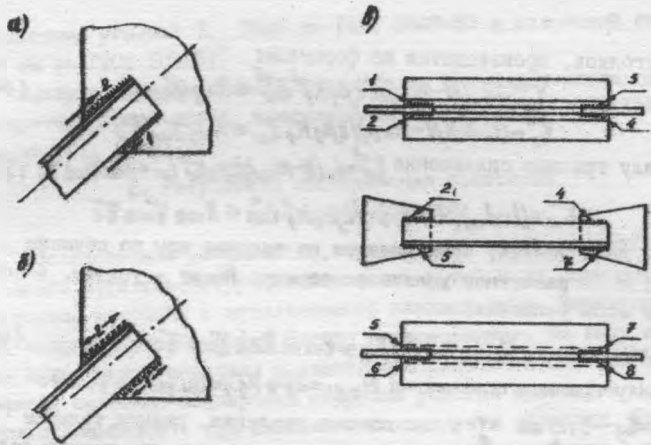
Порядок наложения швов и направление сварки:
